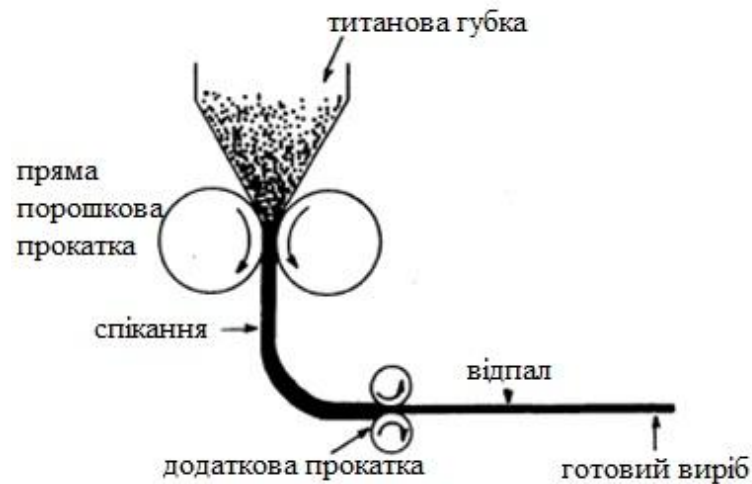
Схема виготовлення листів з титанового порошку [18]
